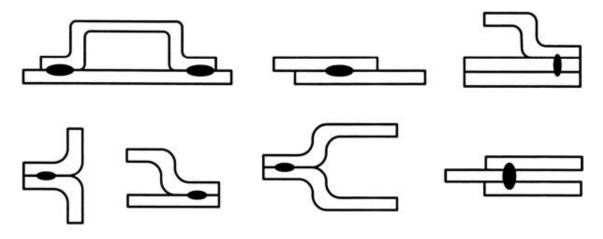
Типы сварных соединений точечной сваркой
